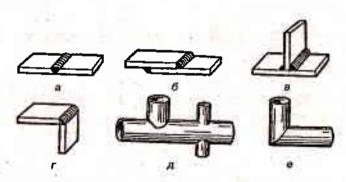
Сварные соединения: а — стыковое; б — нахлесточное; в, д — тавровое; г, е — угловое
